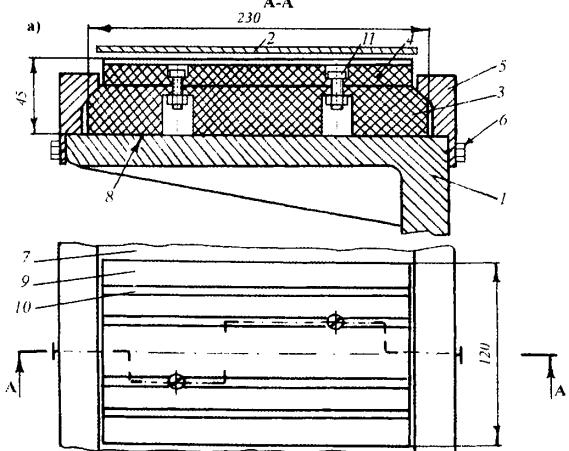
Багатопарний фрикційний вузол модельного стрічково-колодкового гальма: 1 – гальмівний шків; 2 – гальмівна стрічка; 3, 4 – основна та додаткова фрикційні накладки; 5 – знімні реборди; 6 – болти кріплення реборд; 7, 8, 9 – робочі поверхні вузла: шківа, основної та додаткової накладок; 10 – вентиляційні пази; 11 – гвинтові з'єднання
